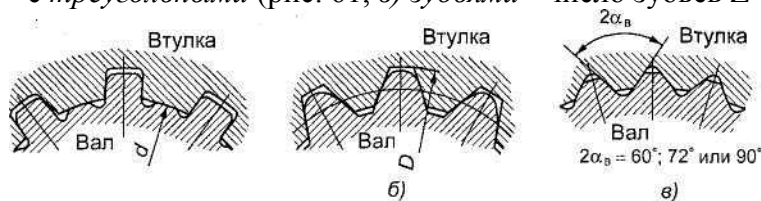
Типы зубчатых (шлицевых) соединений: а — прямобочные зубья; б — эвольвентные зубья; в — треугольные зубья
